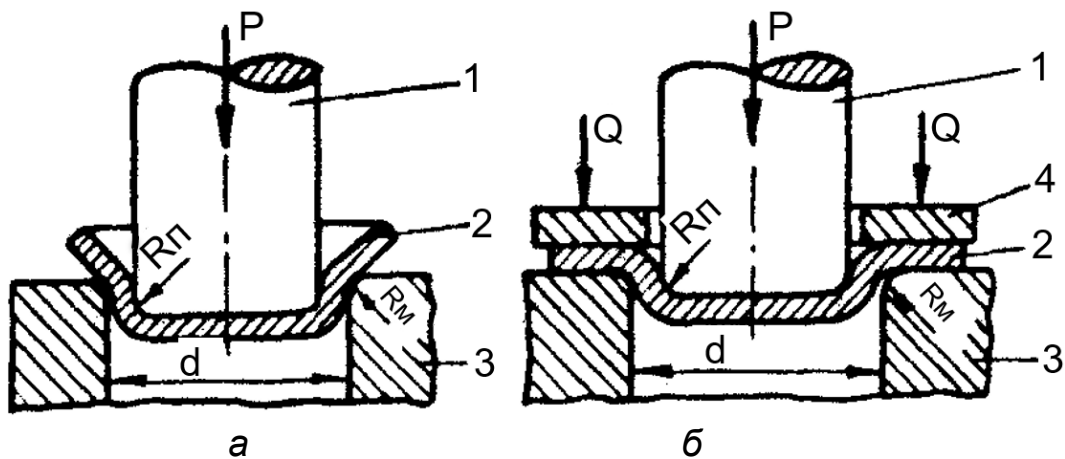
Схеми витягування в штампах: а – без притискання заготовки; б – з притисканням заготовки (1 – пуансон; 2 – заготовка; 3 – матриця; 4 – притискне кільце)
